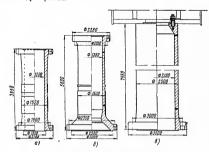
Валы гидротурбин. a — кованый авл;  $\delta$  — сварной вал турбины с расширенным фланцем;  $\delta$  — сварной вал турбины одностью 500 тыс. кет.
